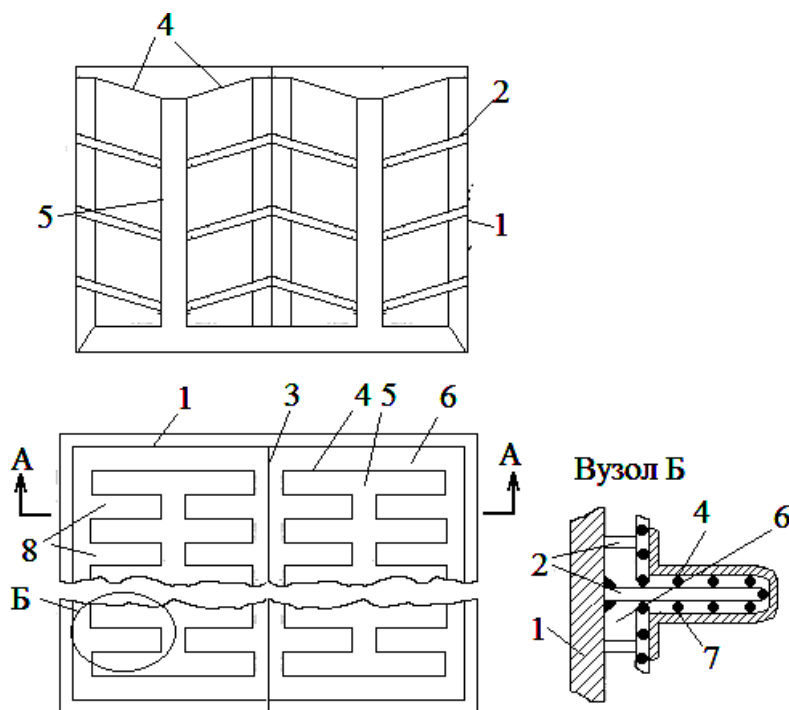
Пристрій корпусу-катода діафрагменного монополярного електролізера: 1 — корпус; 2 — сталеві стрижні-смуги; 3 — сталева перегородка; 4 — катод; 5 — анодна зона; 6 — катодна зона; 7 — діафрагма; 8 — катодні елементи
